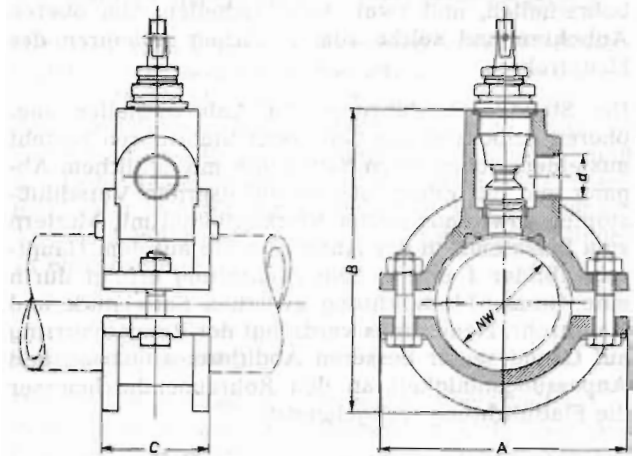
Ventil-Anbohrbrücke für obere Anbohrung mit seitlichem Gewindeabgang für Asbestzement-Röhre
